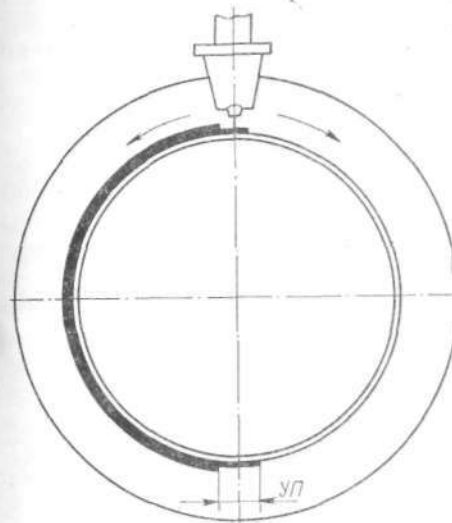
Схема процесса сварки труб за два полуоборота «на спуск».
